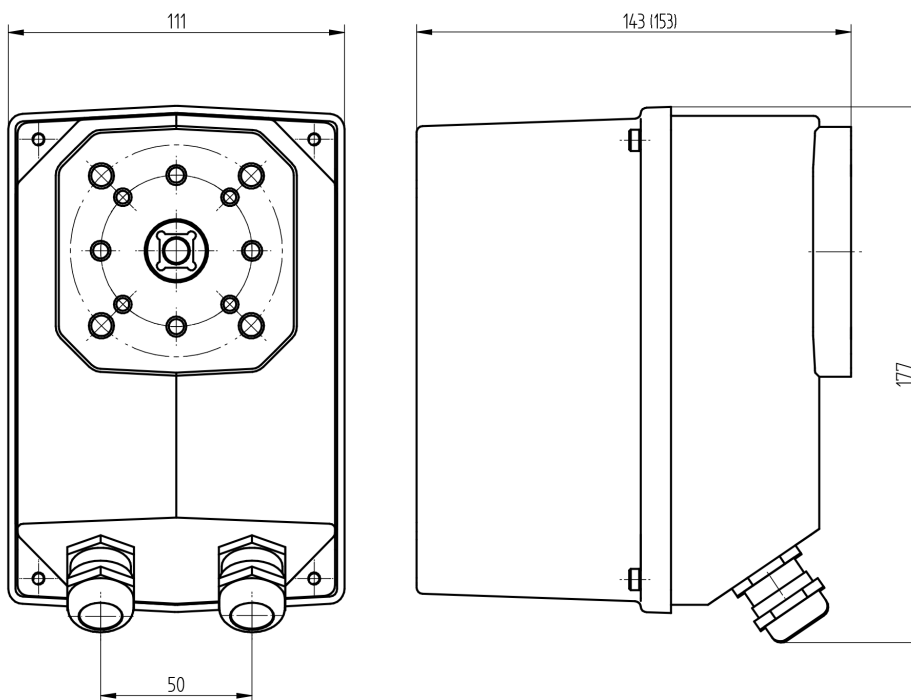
Maßzeichnung Stellantrieb mit Kabeleinführung über Kabelverschraubungen
